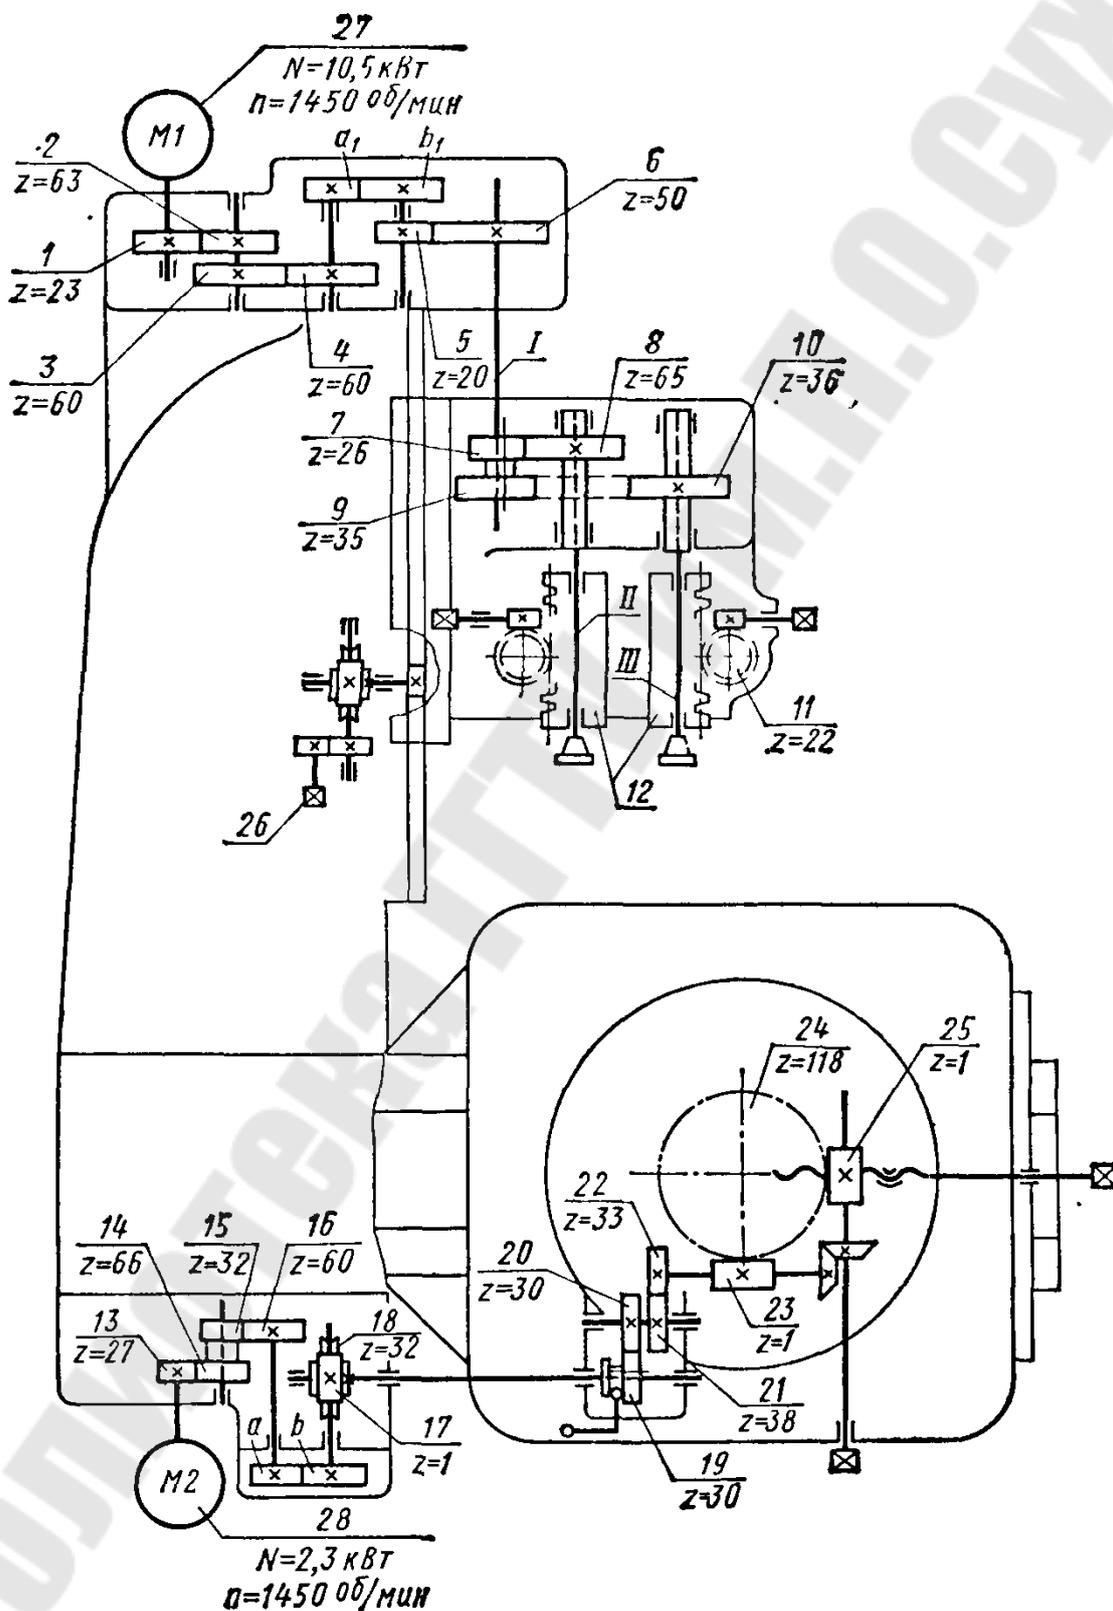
Кинематическая схема карусельно-фрезерного станка
